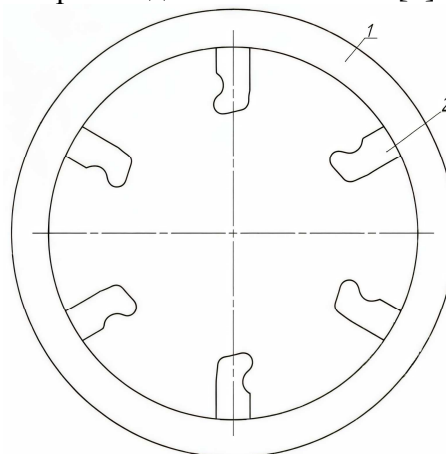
Упрощенная схема вращающейся печи с полками: 1 – корпус; 2 – полки («сапожки»)
